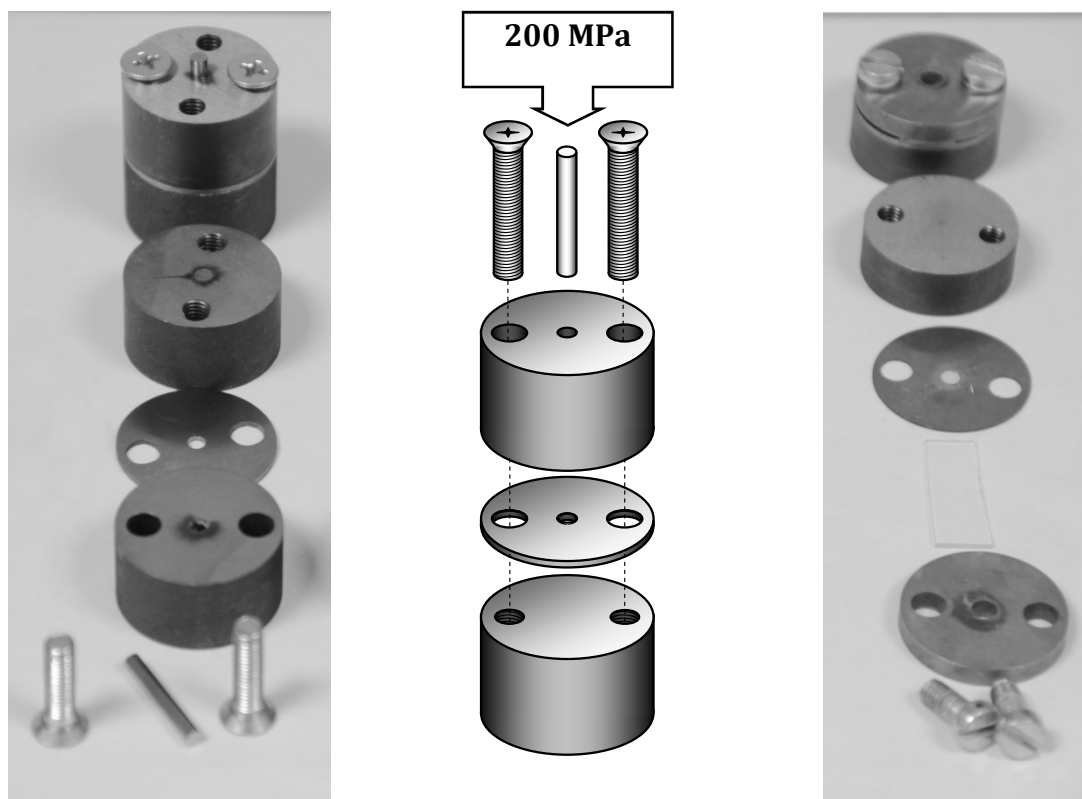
Фото сборки для прессования (слева), схема сборки для прессования (в центре), фото сборки для инициирования (справа).
